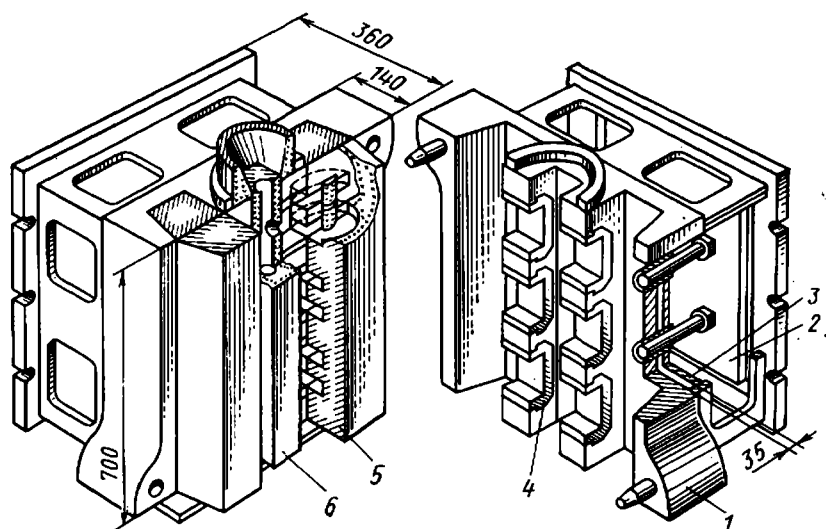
Схема устройства многоместного кокиля для литья бил из стали 110Г13Л
